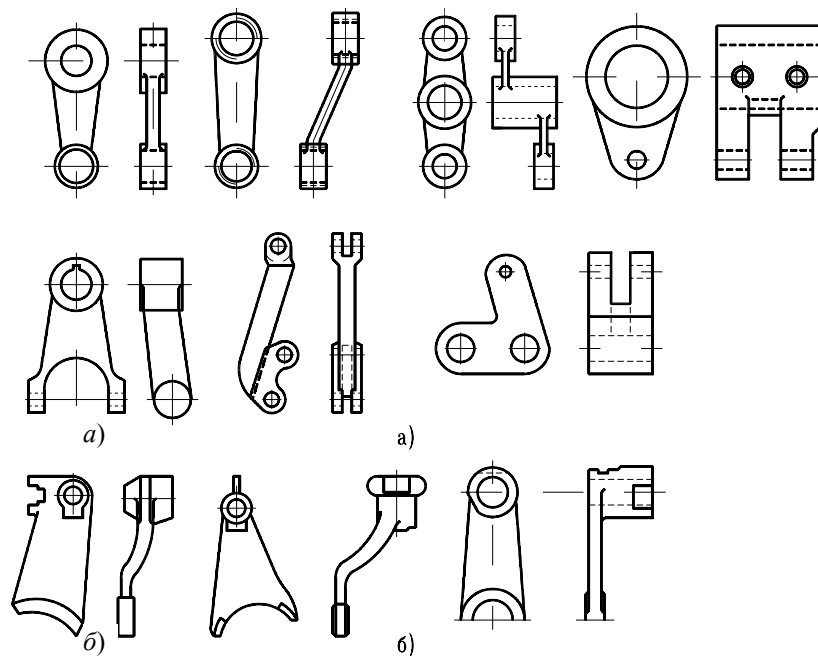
Конструктивные разновидности рычагов, вилок и шатунов
